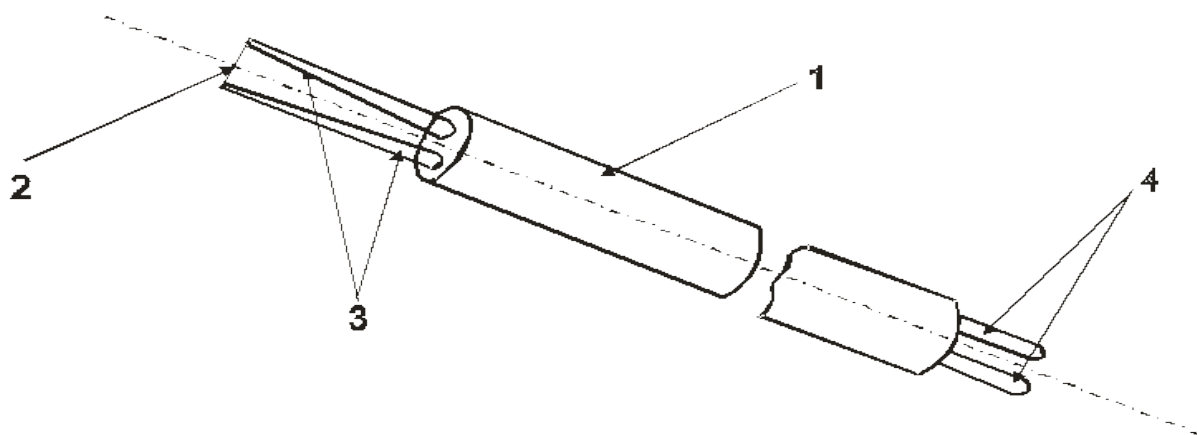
Конструкция датчика: 1 – корпус, 2 - нагреваемая нить, 3 – держатели, 4 - токоподводы.
